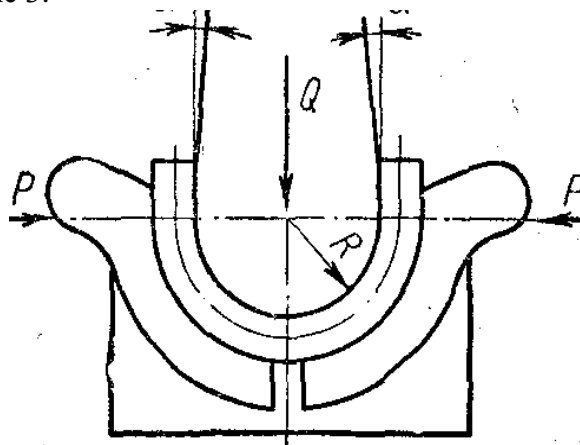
Схема гибки волноводной трубы в штампе с клиновыми ножами
